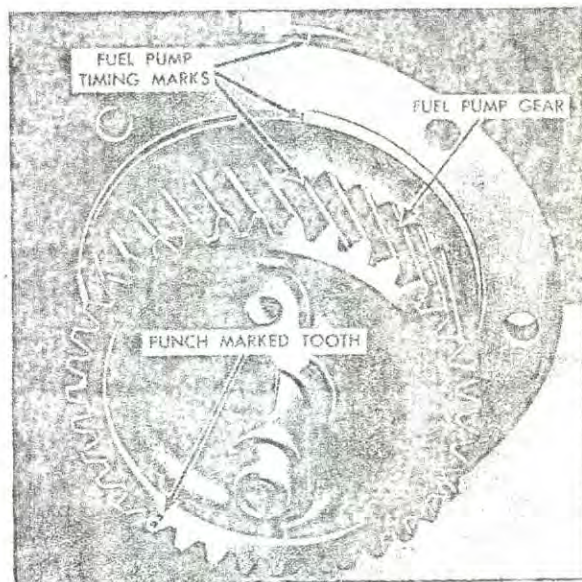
Marcas de reglaje en el engranaje y caja de la bomba de combustible
